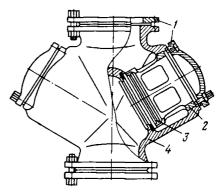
Обратный клапан компрессора 4BM10-100/8:
